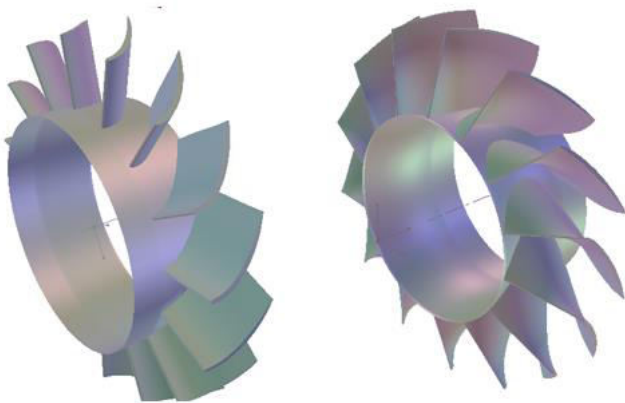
Disegno 3D di rotore e statore ricavati con BladeGen
